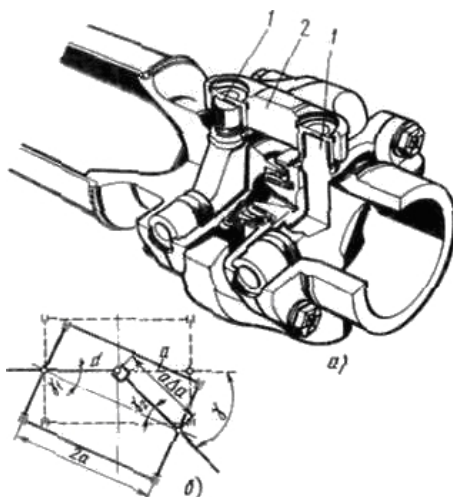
Сдвоенный карданный шарнир: а — конструкция; б — схема; 1 — шарниры; 2 — вилка
